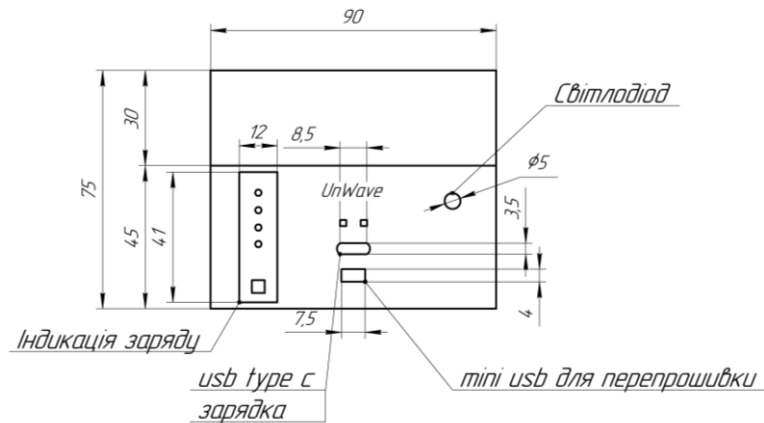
Корпусне креслення приладу UnWave, вид збоку
